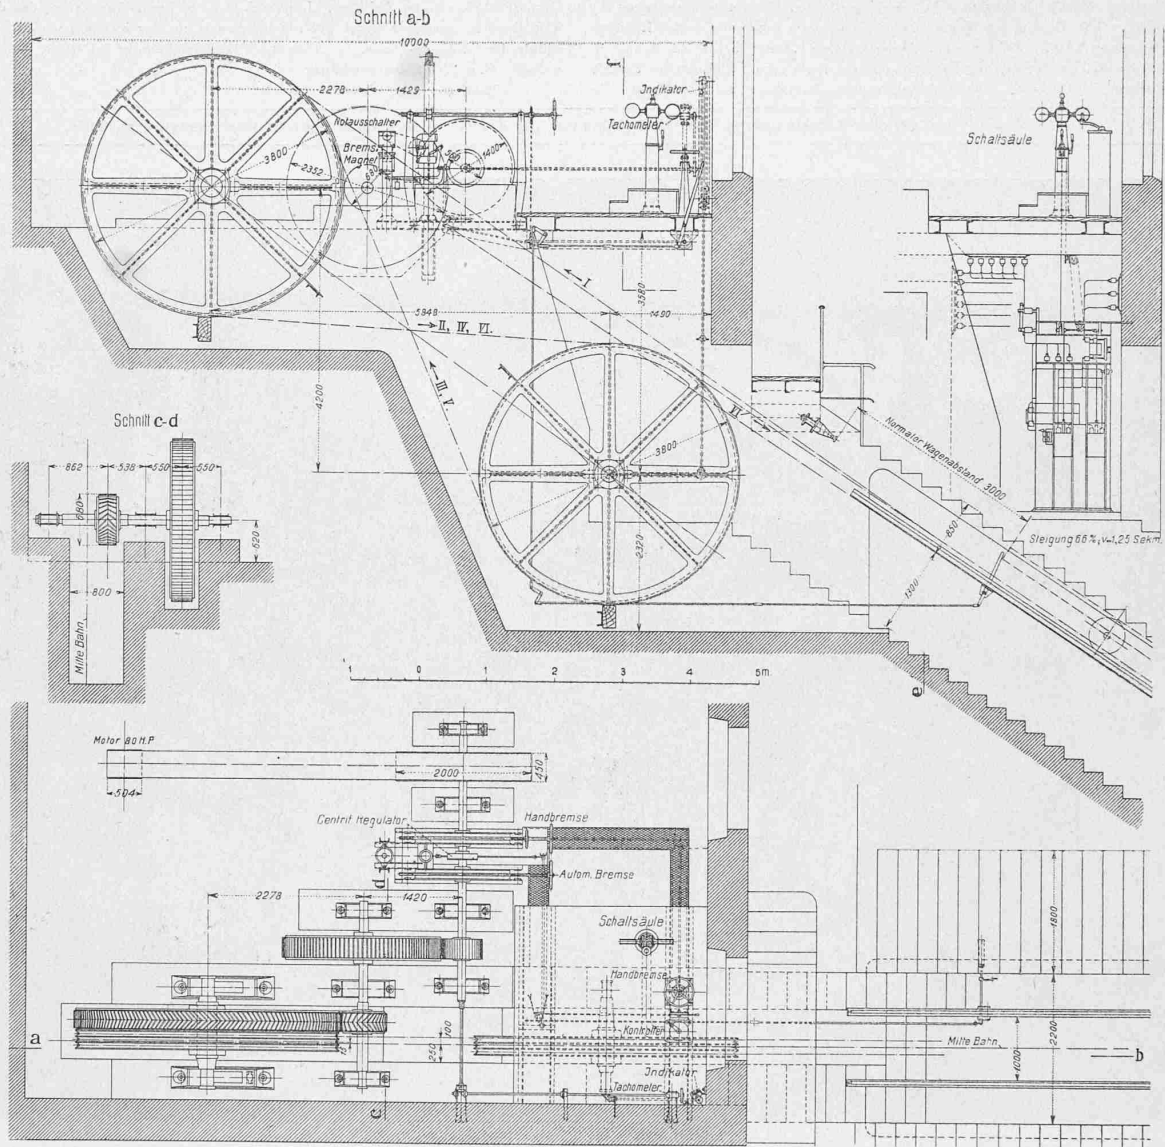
Windwerk der I. Sektion auf der Antriebsstation Schwandegg. — Grundriss und Schnitte. — Masstab 1 : 100.
